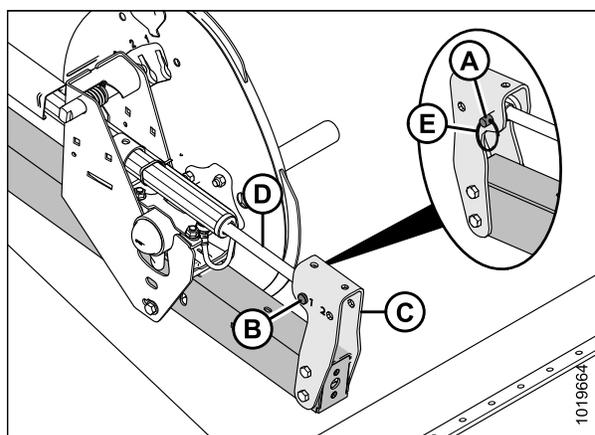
Цилиндр правого рычага мотовила в заднем положении
